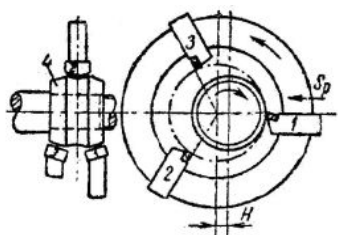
Схема обработки с применением поперечной подачи (1-3- резцы резцовой головки; 4- обрабатываемая деталь).
